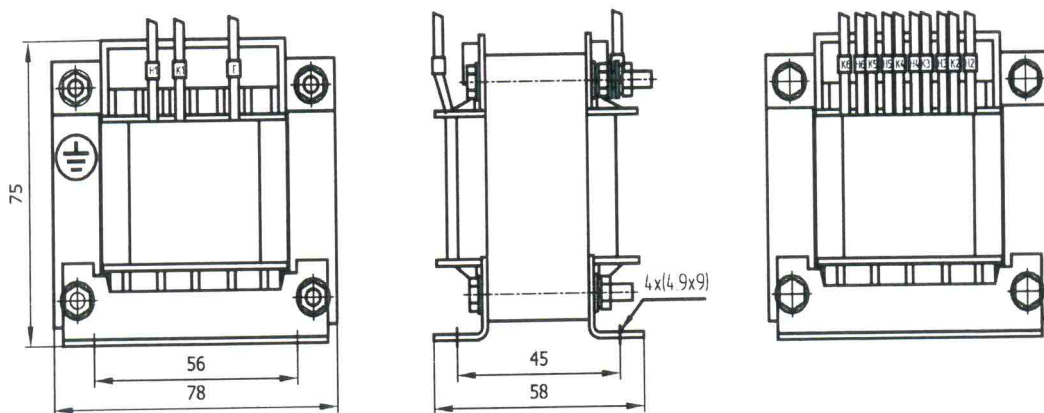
Габаритный чертёж трансформатора Т-846
